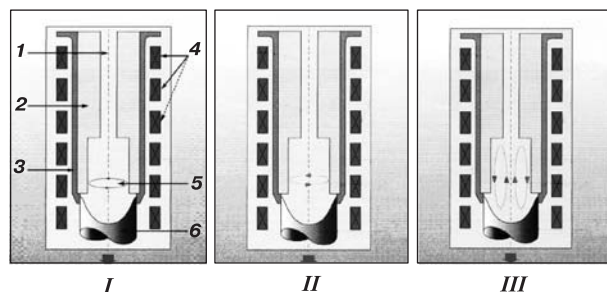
Установки магнитогидродинамического перемешивания разных компаний (*I–III*): 1 — питающая труба; 2 — огнеупорная футеровка; 3 — металлический кристаллизатор; 4 — катушки индуктивности, составляющие линейный индуктор; 5 — зона перемешивания; 6 — затвердевшая заготовка
